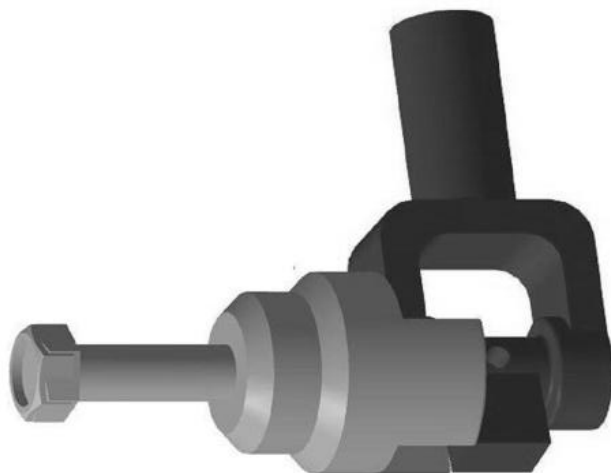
Приспособление для сборки разборки карданных шарниров
